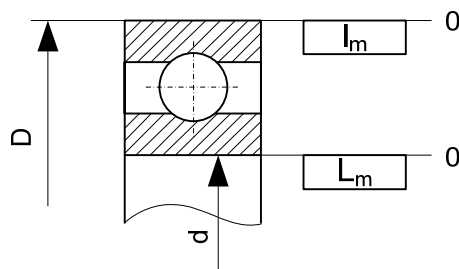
Поля допусков присоединительных размеров подшипника
